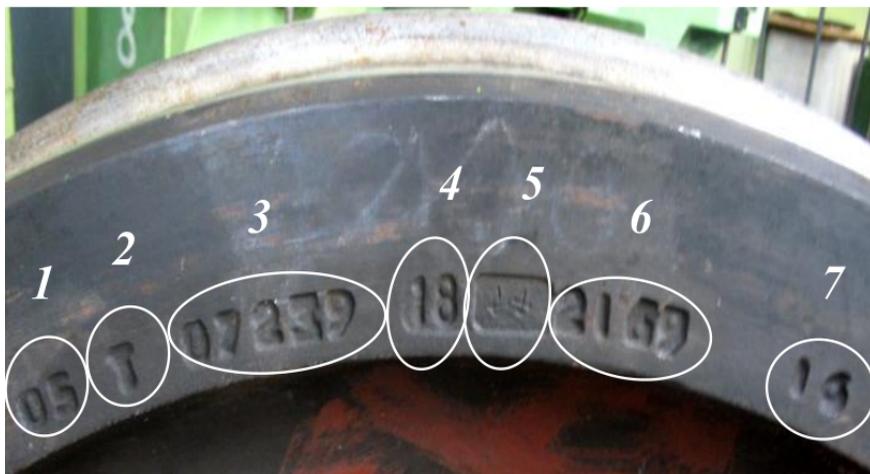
Клейма и знаки маркировки, относящиеся к изготовлению колеса:
